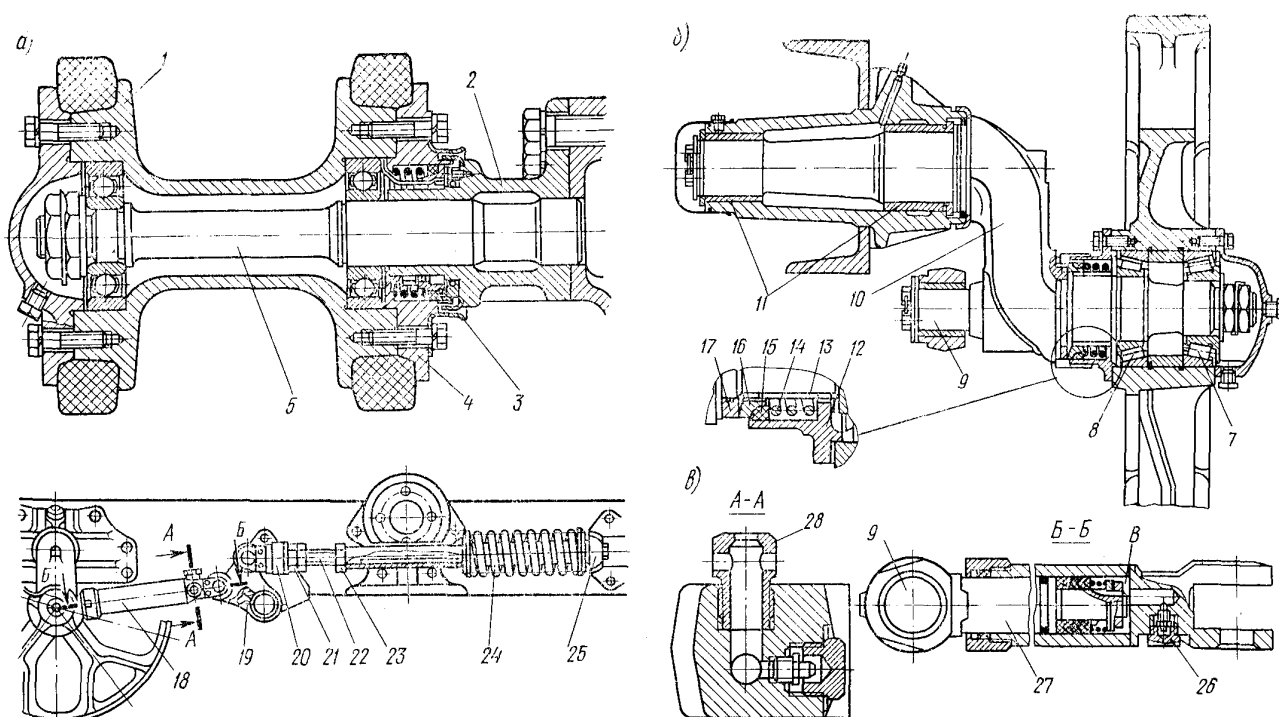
Поддерживающий ролик (а), направляющее колесо (б) и натяжное устройство (в) гусеничного трактора
